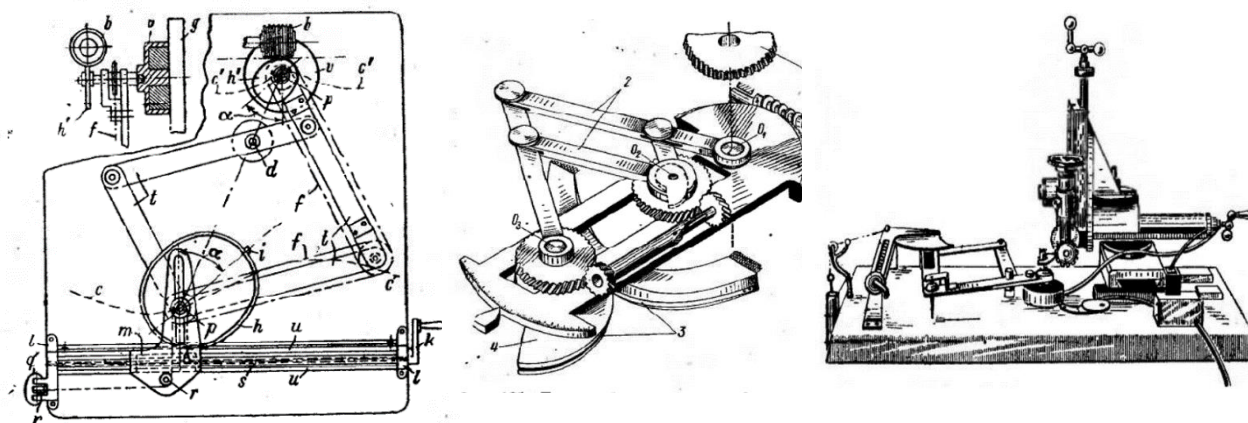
Приспособление для нарезания некруглых зубчатых колес (1956 г.) [7]
